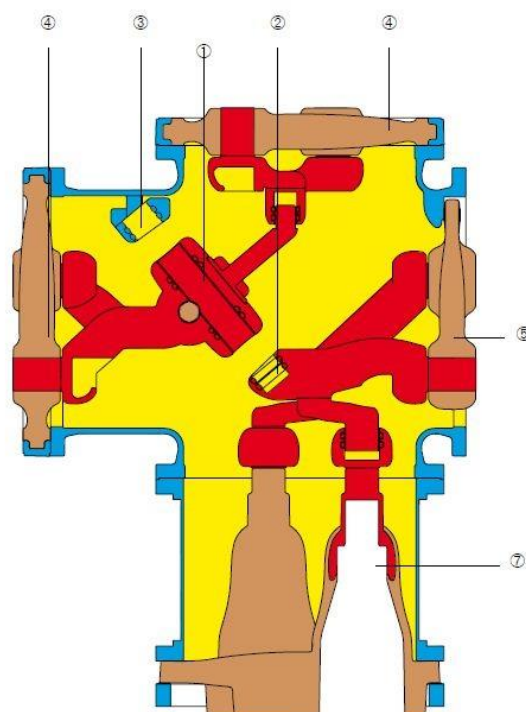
Шинный и фидерный комбинированные разъединители-заземлители: 1 – трехпозиционный механизм; 2 – контакт разъединителя; 3 – контакт заземлителя; 4 – барьерный изолятор; 5 – опорный изолятор;
